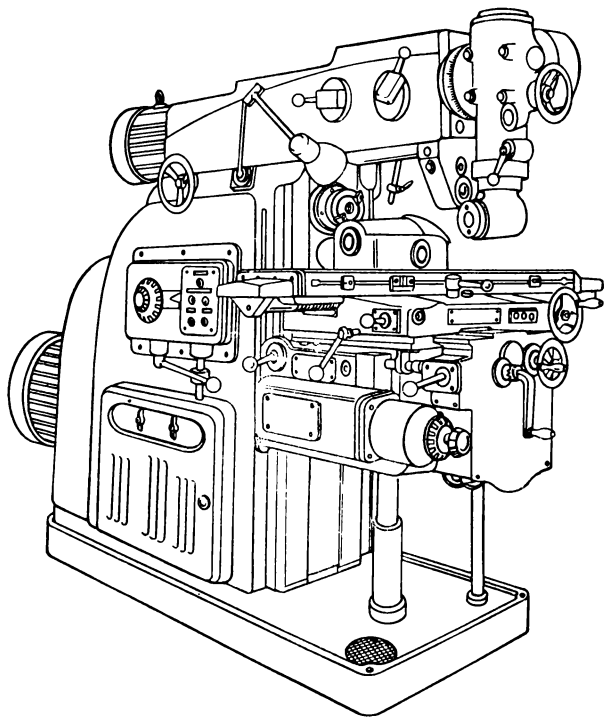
Широкоуниверсальный фрезерный станок 6М82Ш
